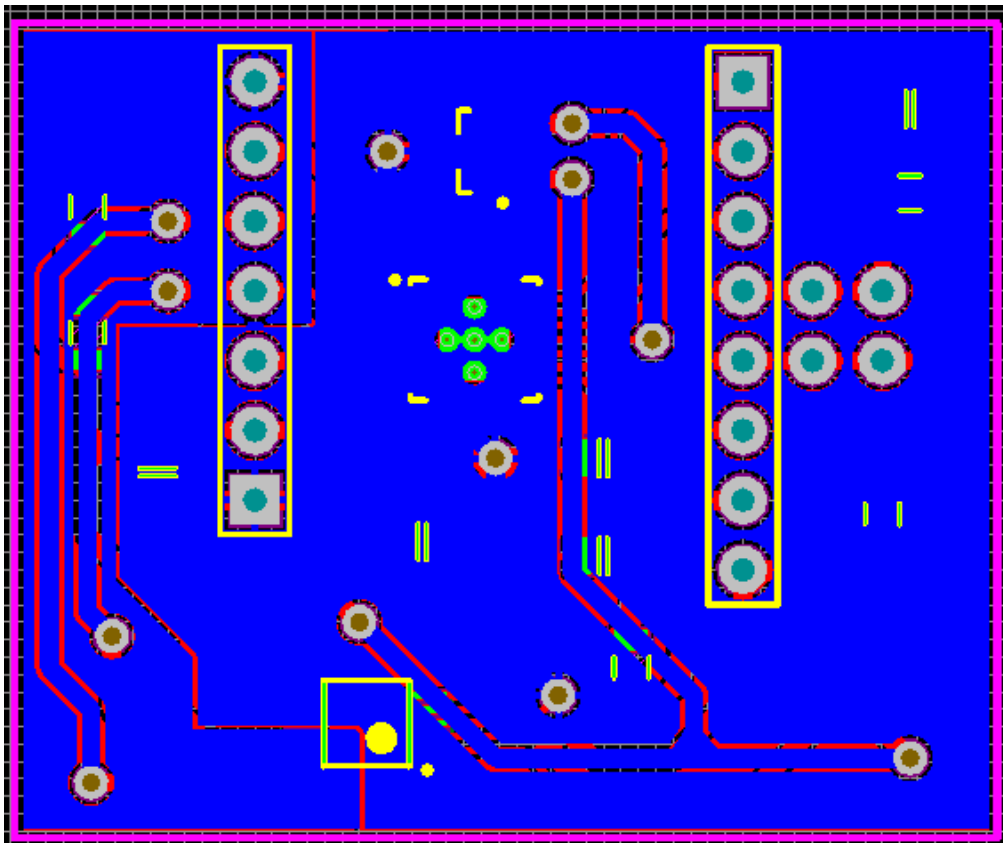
Capa inferior de la PCB del circuito impreso final
